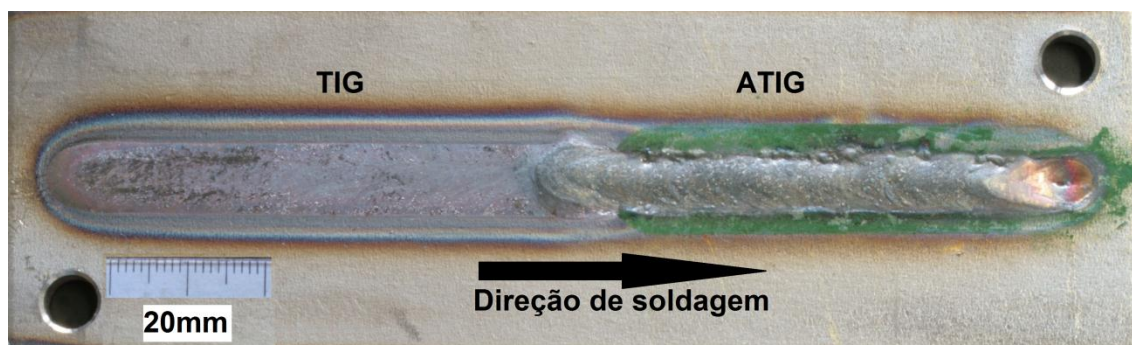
Exemplo de corpo de prova após a soldagem
